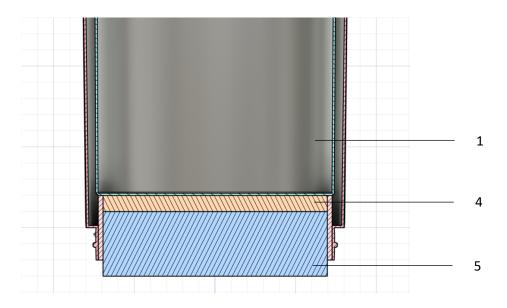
Detalle Batería, Celda Peltier (4) y Batería (5).
